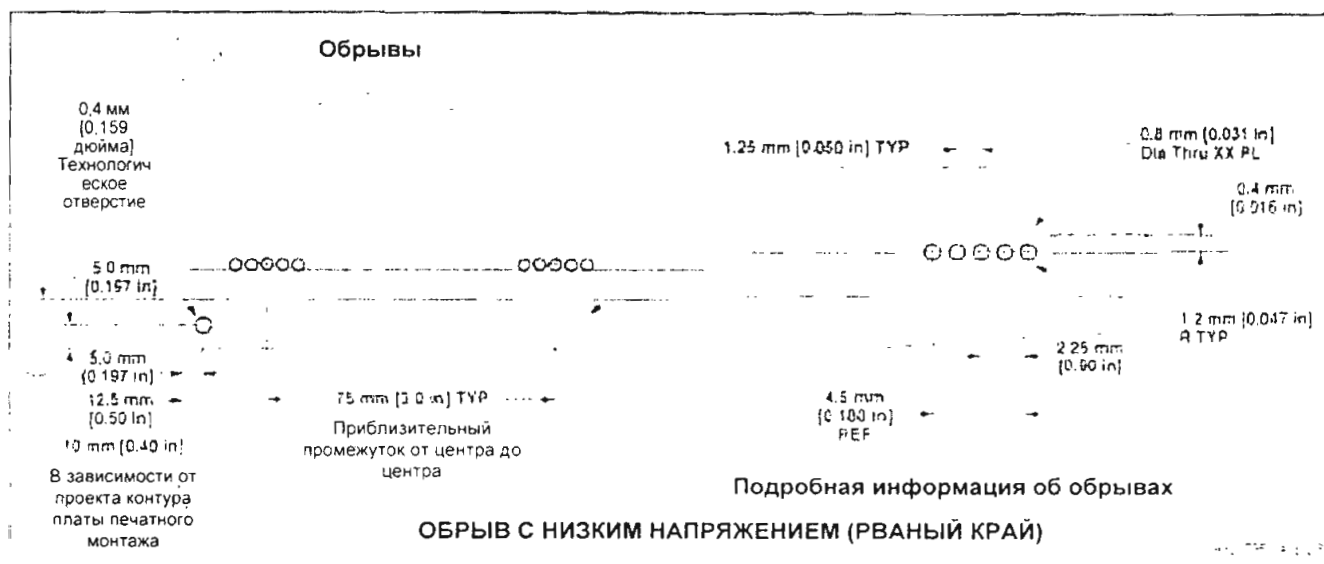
Обрыв (проложенный образец) с проложенными пазами
